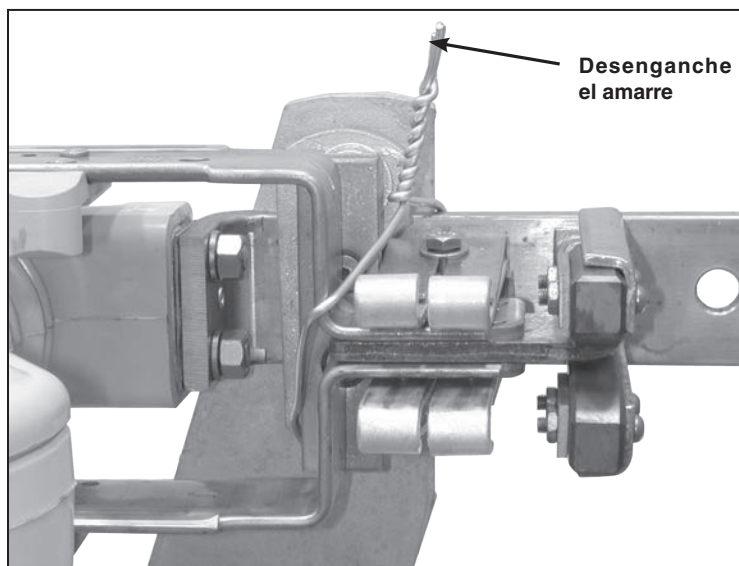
Desenganche del amarre en el ensamble del contacto estacionario principal.
